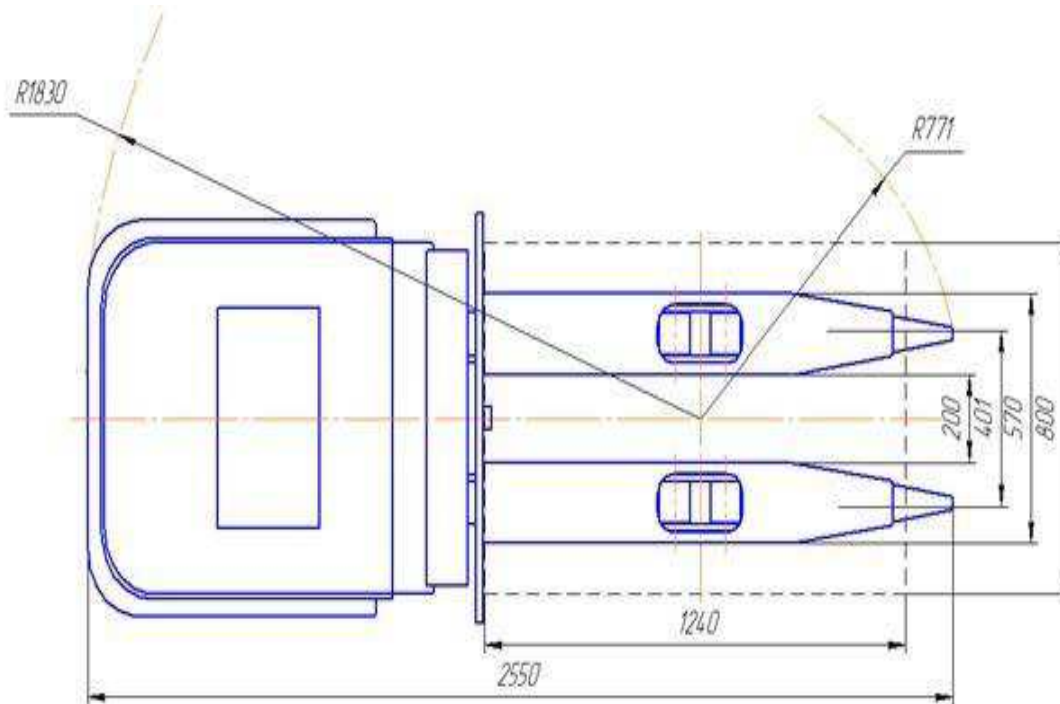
Вертикальный вид автоматического транспортного устройства
